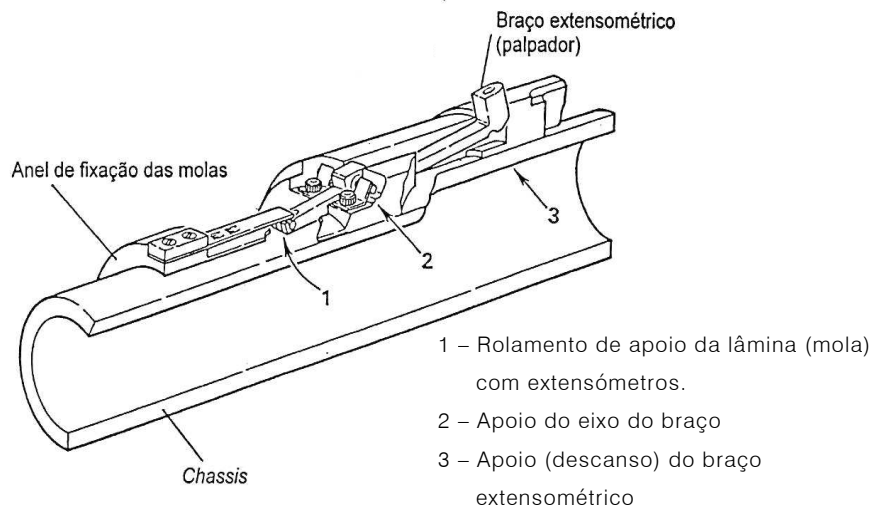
7 - Chassis do CSBP, mostrando um conjunto braço e palpador, adaptado de Marques (1997)
